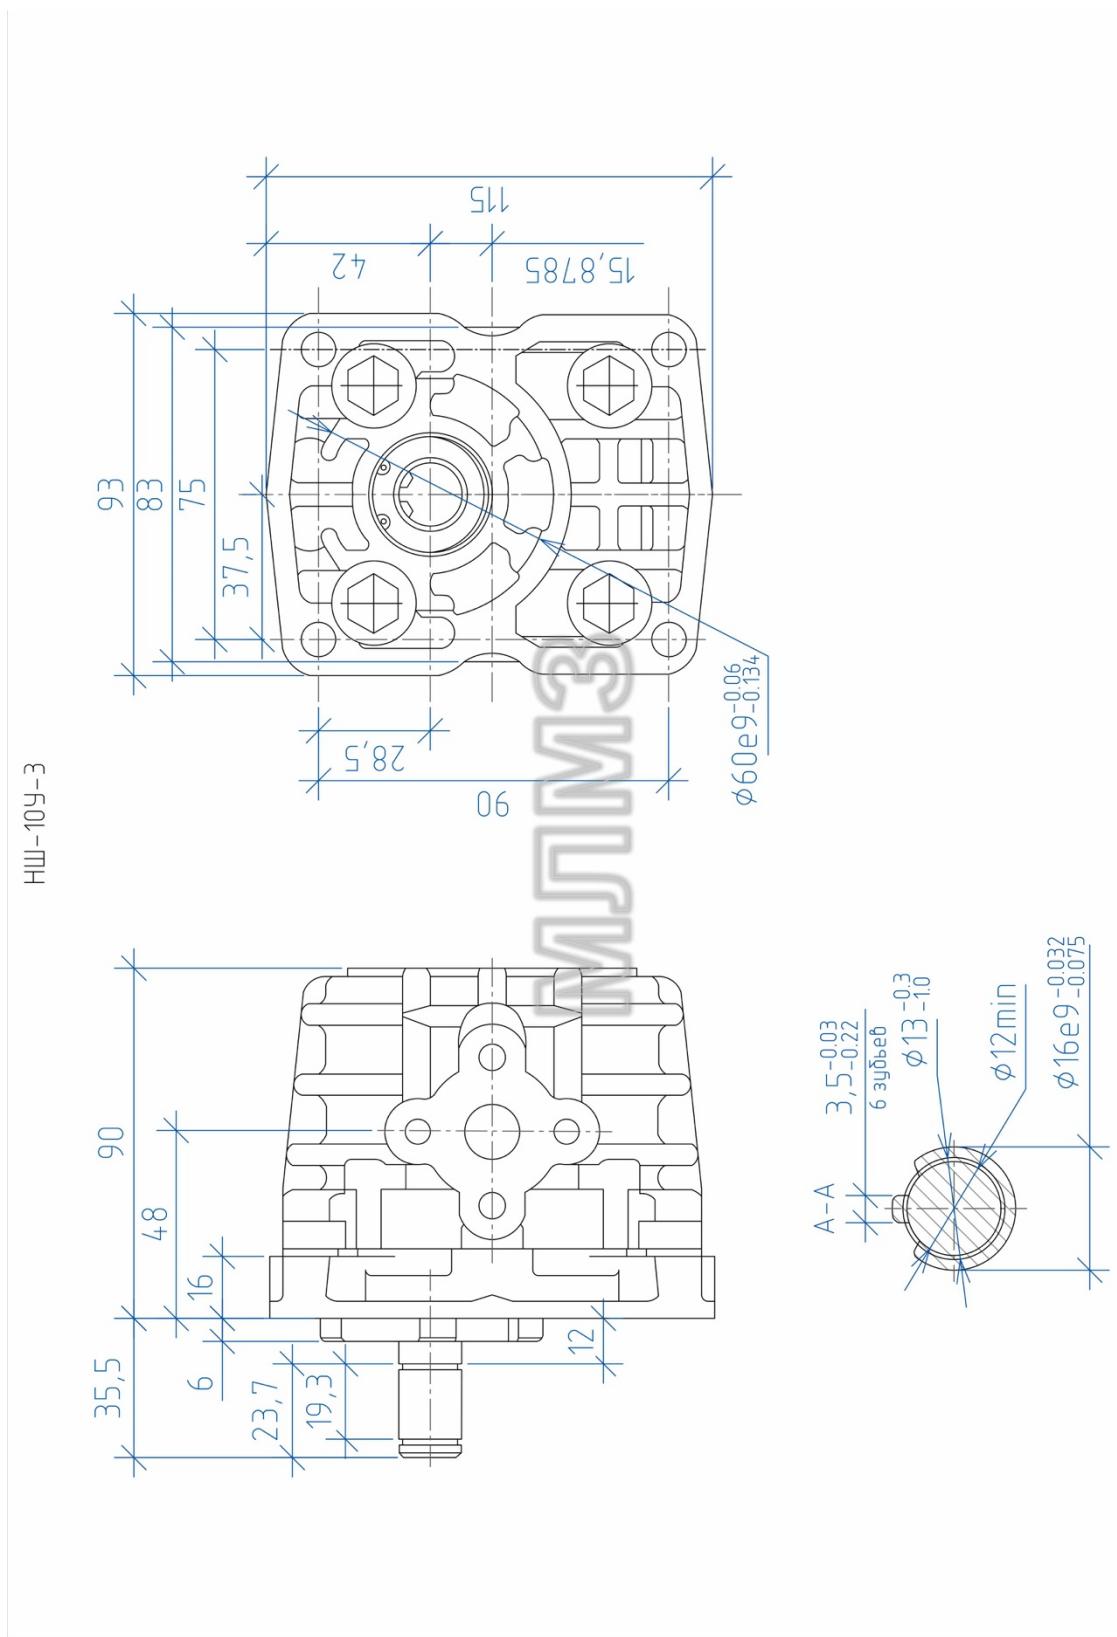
Насосы шестеренные НШ10У-3, НШ10У-3Л. Габаритные и присоединительные размеры.
